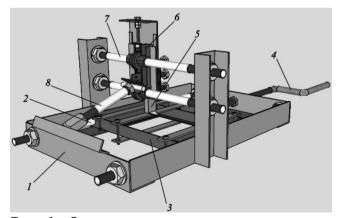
Стенд резания изотропного материала: 1 – рама; 2 – направляющие перемещения рамки; 3 – рамка; 4 – винт; 5 – резец; 6 – резцедержатель; 7 – направляющие перемещения резцедержателя; 8 – съемный упор
